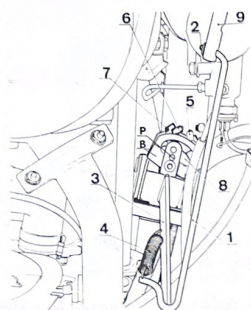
Vista en la parte izquierda del compartimento del motor, del conjunto de mando del freno de mano.
